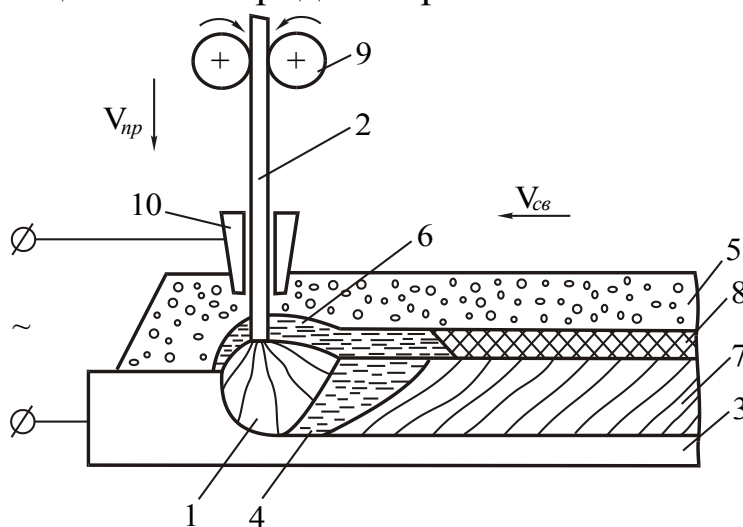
Схема процесса автоматической дуговой сварки под флюсом
